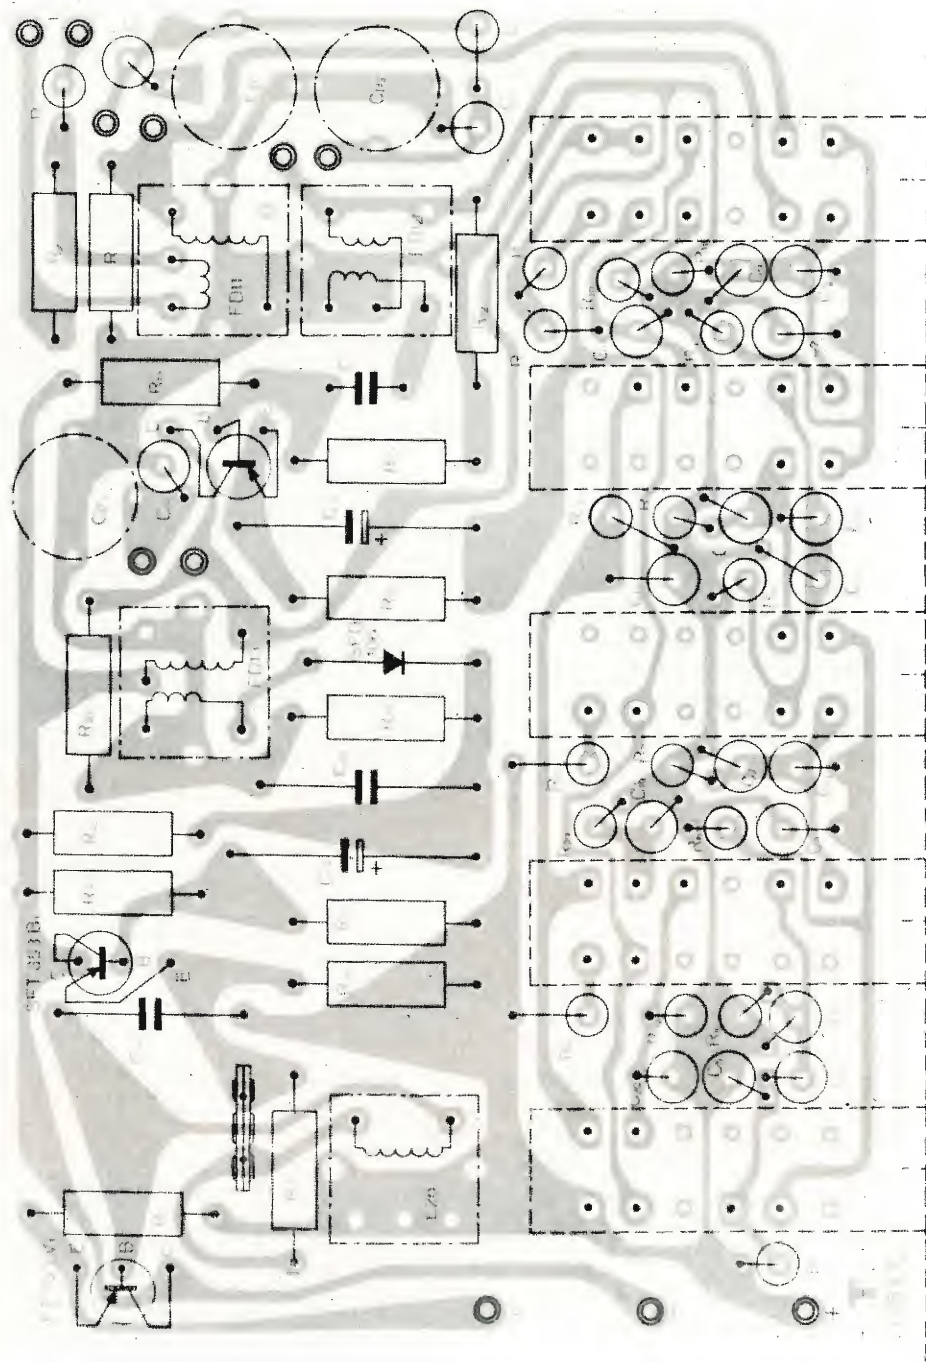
Circuito stampato e montaggio dei componenti del ricevitore.
